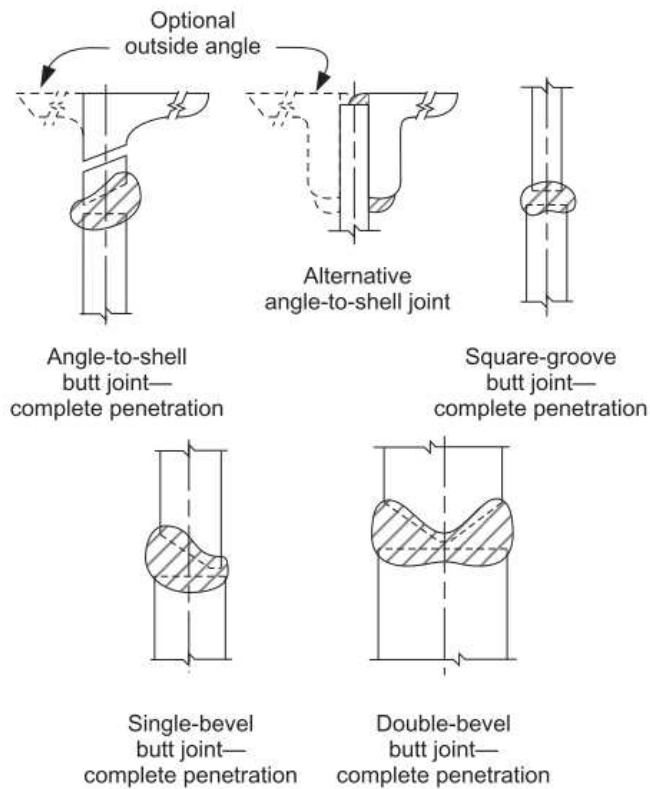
Soldaduras a tope para juntas verticales.
